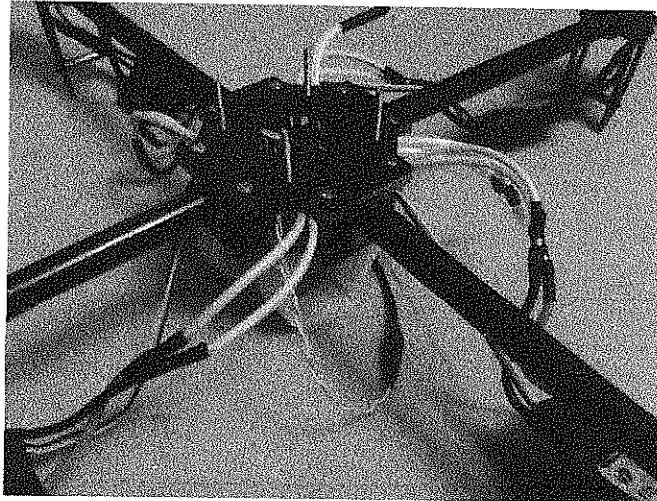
Detalle Estructura Armada con PCB de Potencia.
